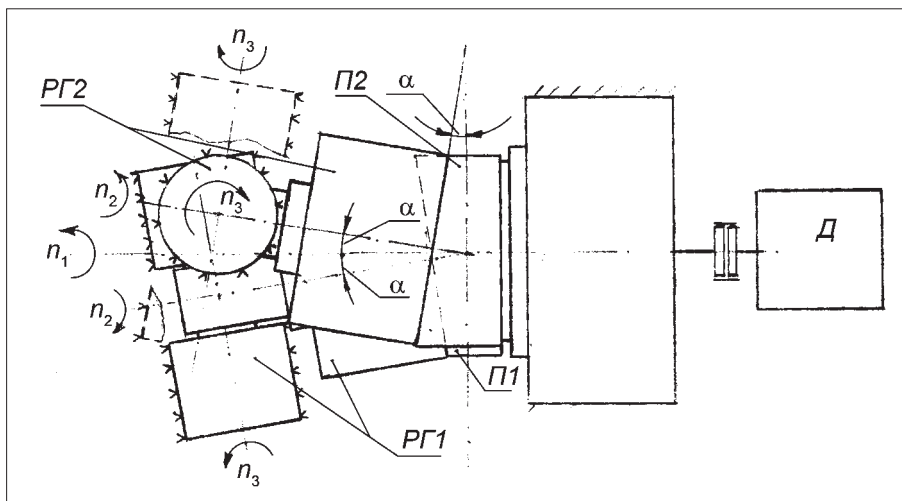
Вид сбоку на планетарный исполнительный орган:
